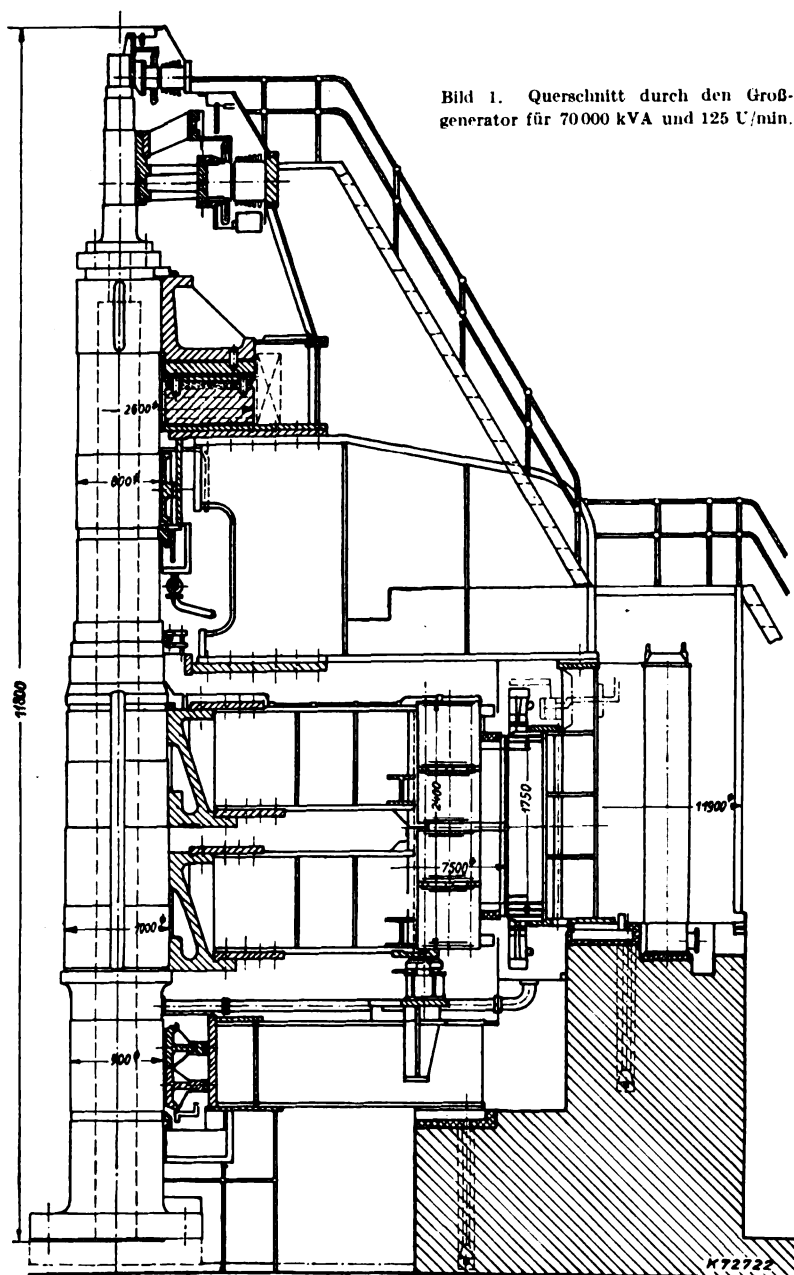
Querschnitt durch den Großgenerator für 70000 kVA und 125 U/min.
